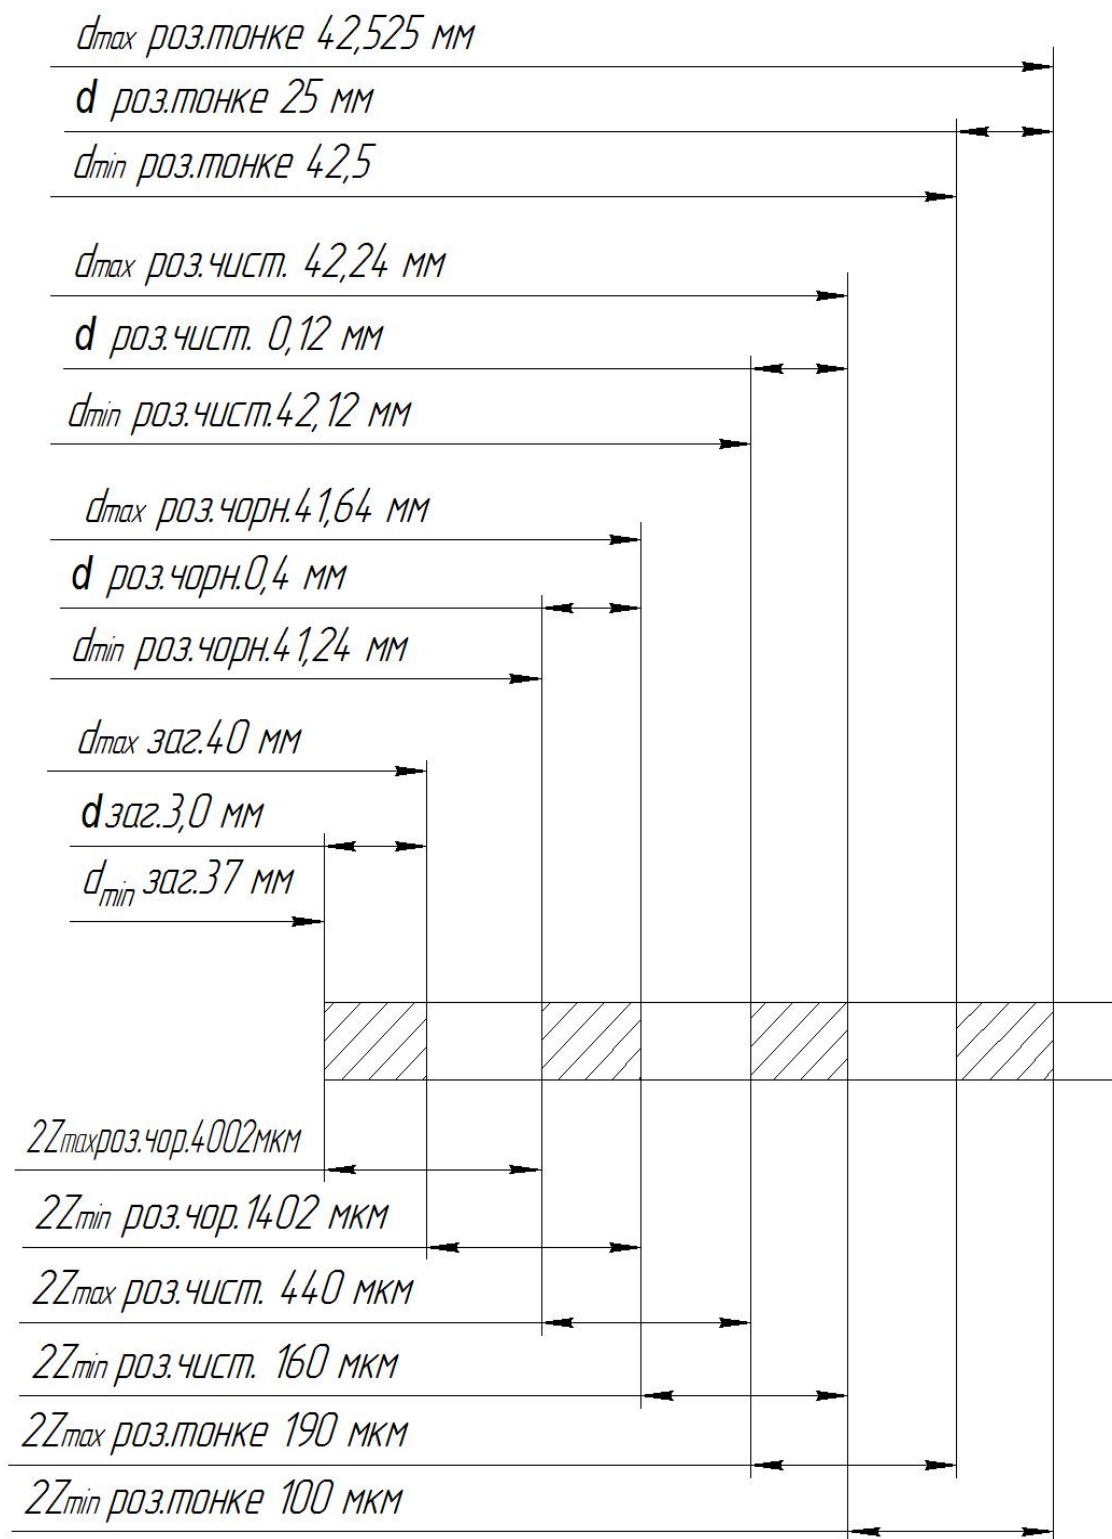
Схема графічного розташування припусків і допусків для поверхні $\varnothing 42,5^{+0,025}$.
